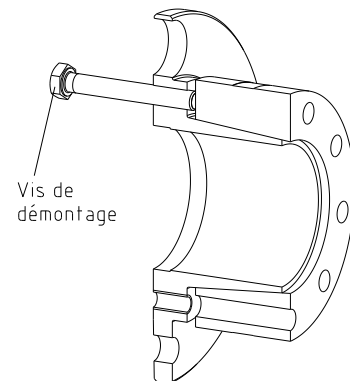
Démontage du moyeu à frette de serrage 6.5
